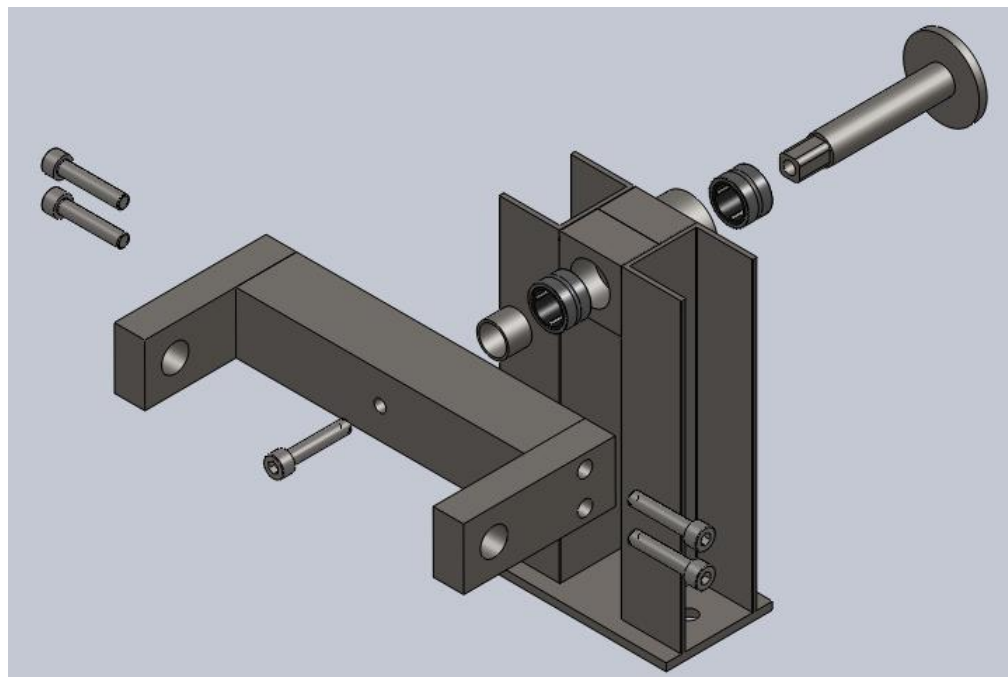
14. Explosionado soporte delantero potro de soldadura
